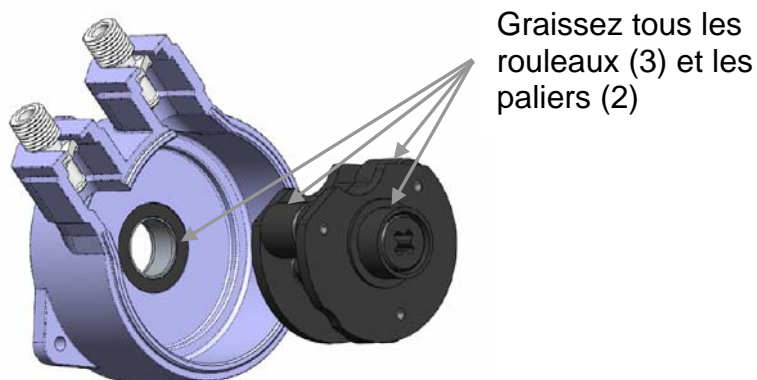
Tête de pompe / Assemblage rotor retiré
